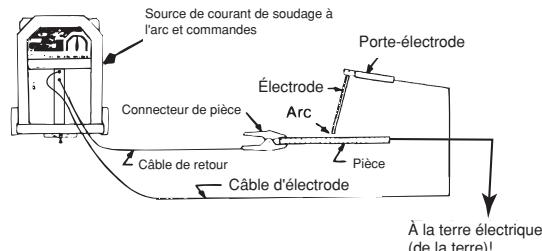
Circuit de soudage pour le procédé SMAW
